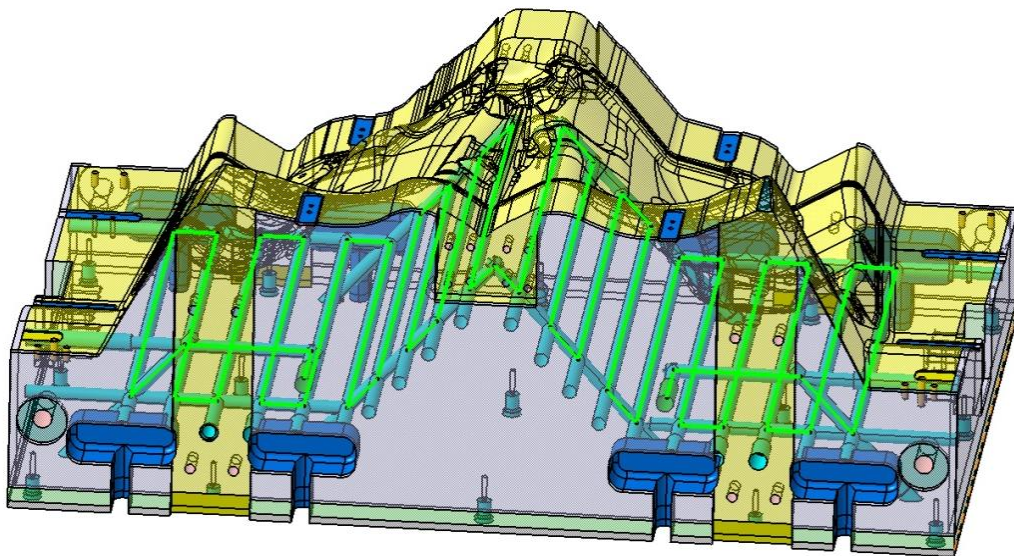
Porovnání obou ploch obr. č. 13-5 a 13-6
